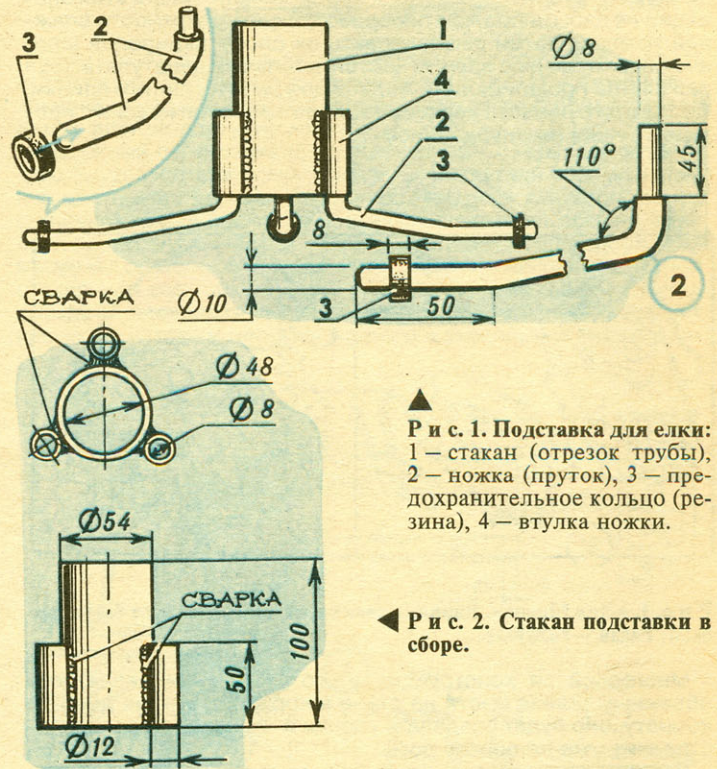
Подставка для елки: 1 — стакан (отрезок трубы), 2 — ножка (пруток), 3 — предохранительное кольцо (резина), 4 — втулка ножки.
